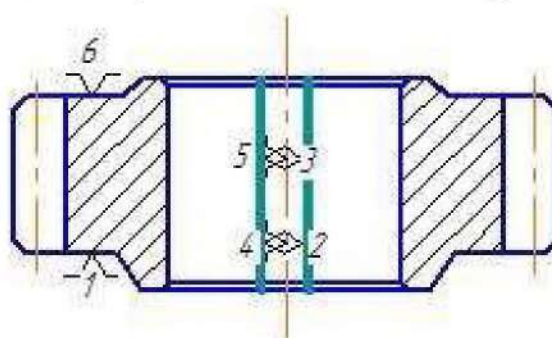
Схема базування заготовки на довбальній операції 020
